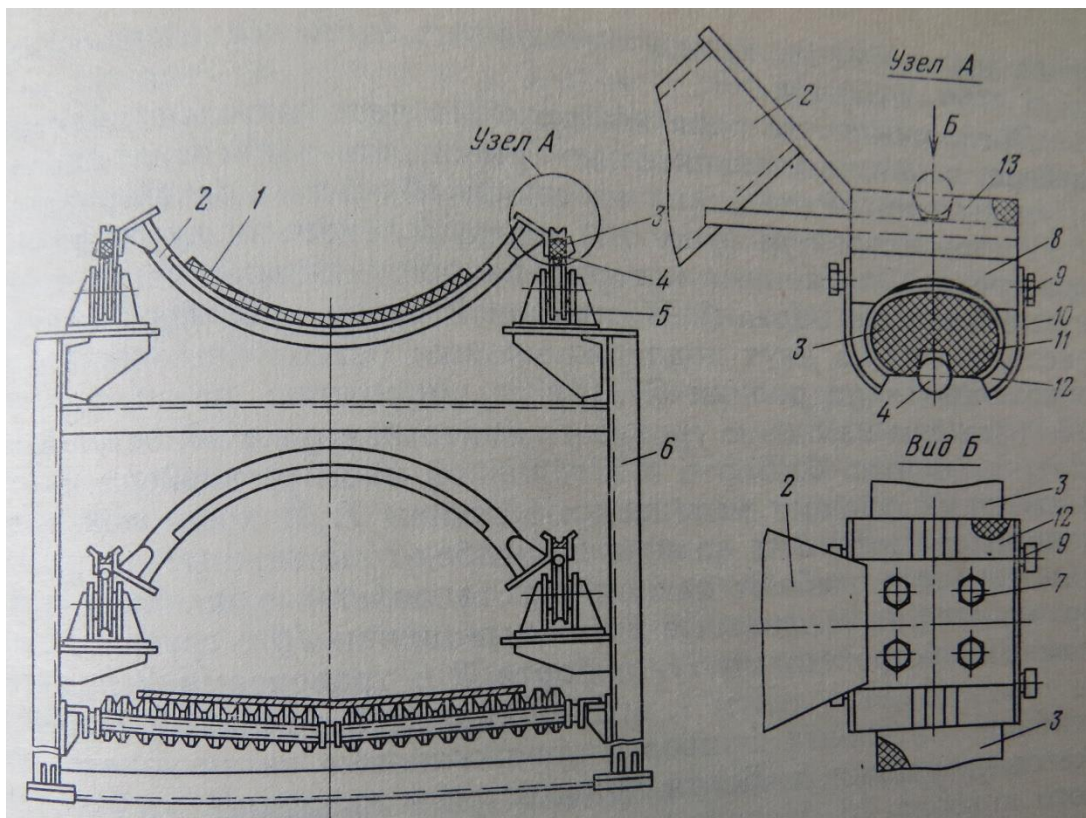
Схема стрічково-канатного конвеєра для транспортування крупношматкових вантажів:
